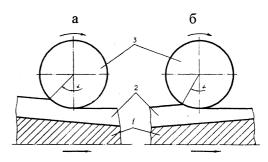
Схемы прокатки: a-c нарастающим; 6-c убывающим обжатиями; 1- профильная оправка; 2- заготовка; 3- прокатный валок
